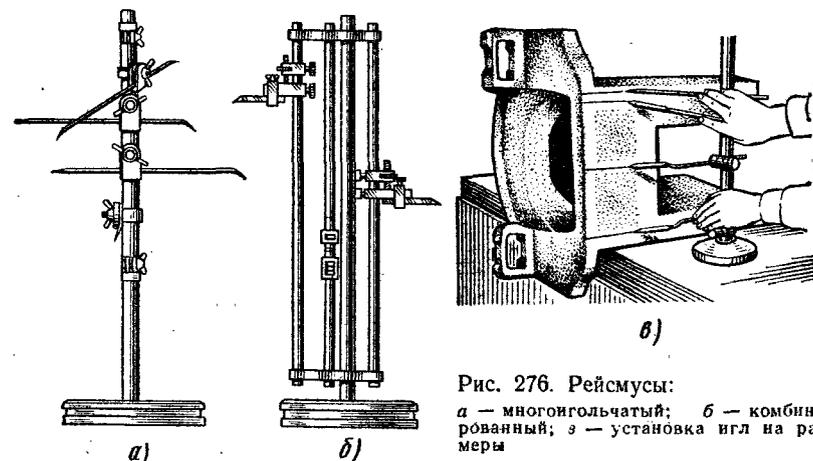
Рейсмусы: а — многоигольчатый; б — комбинированный; в — установка игл на размеры
